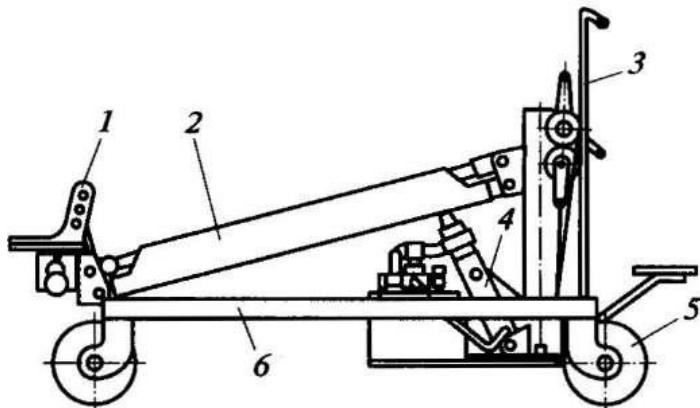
Тележка для снятия и постановки рессор: 1- подхват для рессор; 2 — стрела; 3 — рукоятка; 4 — гидроцилиндр; 5— колесо; 6 — продольная балка
